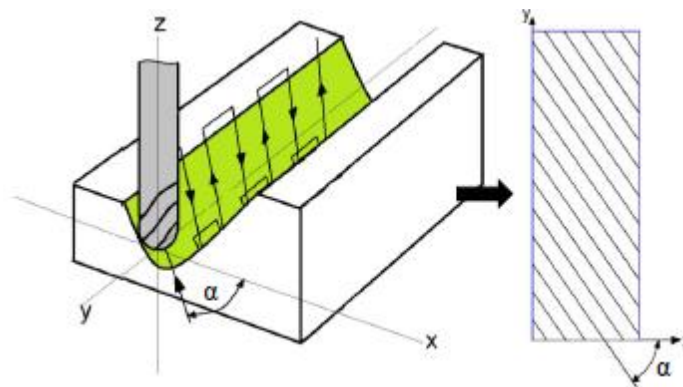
Схема фрезерування формуючої поверхні з траєкторією фрезерування під кутом  $\alpha$
